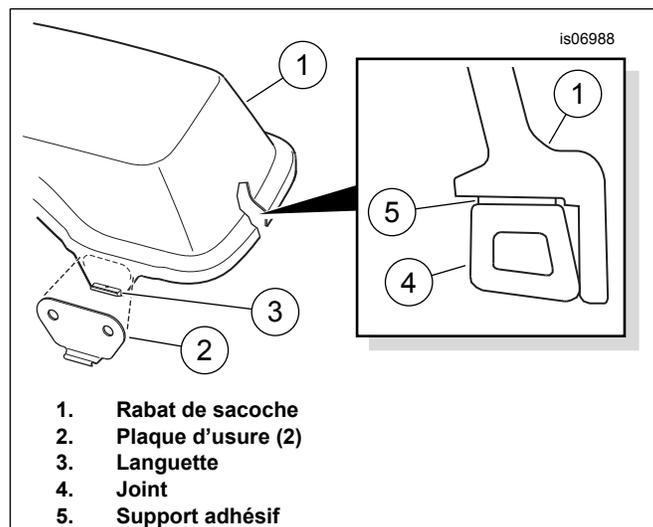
Assembler les plaques d'usure et le joint sur le rabat de sacoche
